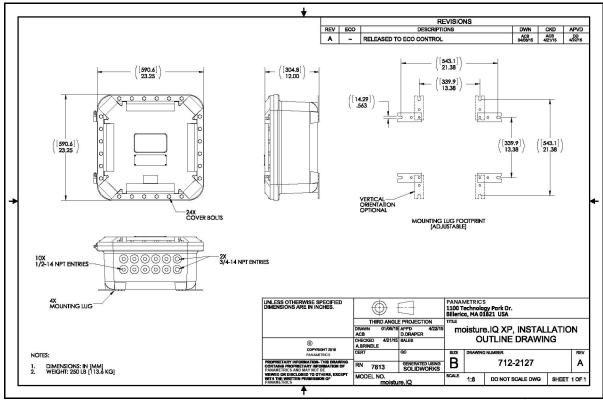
Desenho da instalação de XP (Desenho 712-2127\_revA, SH 1 de 1)
